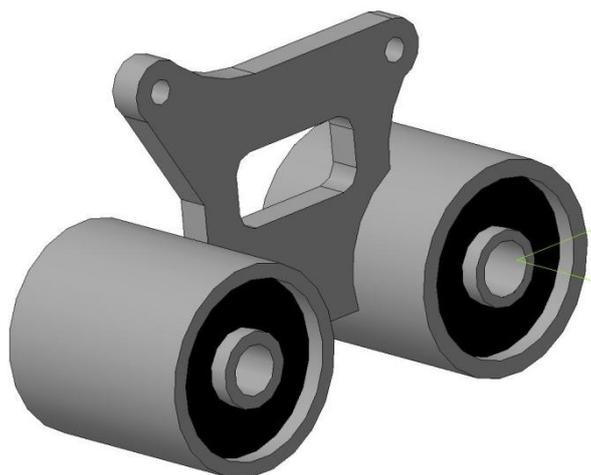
Предлагаемая конструкция опоры КПП ВАЗ-2101-07
